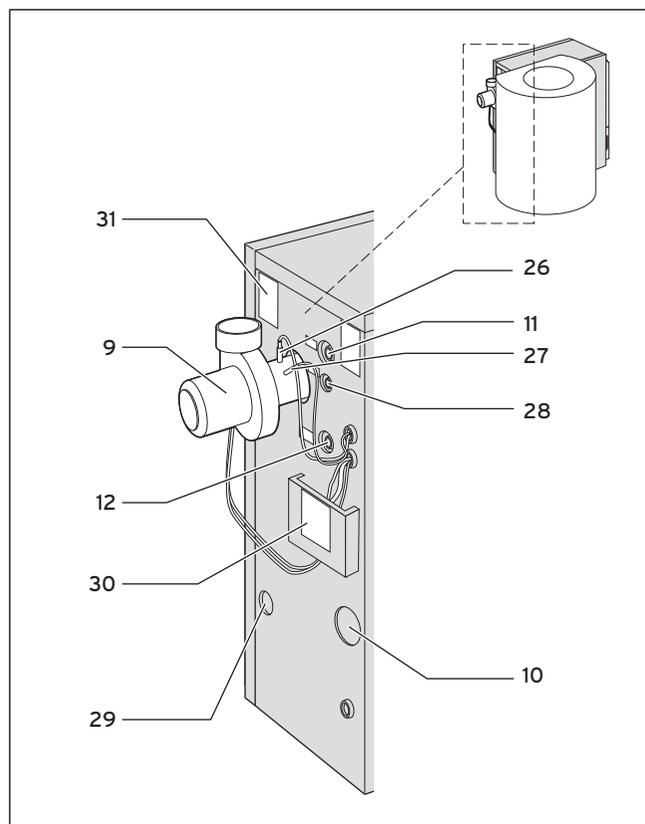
Rückansicht des Pellet-Heizkessels
